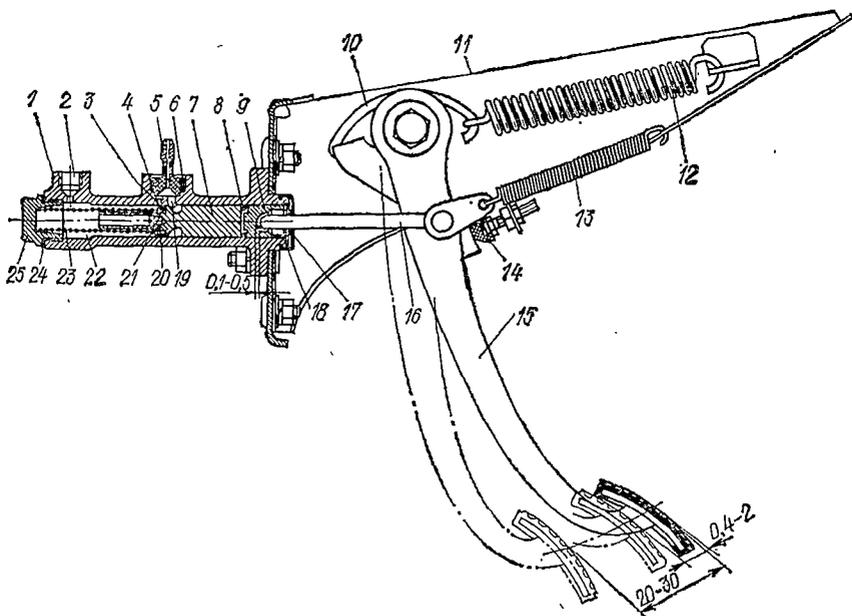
Педаль и главный цилиндр привода сцепления:
